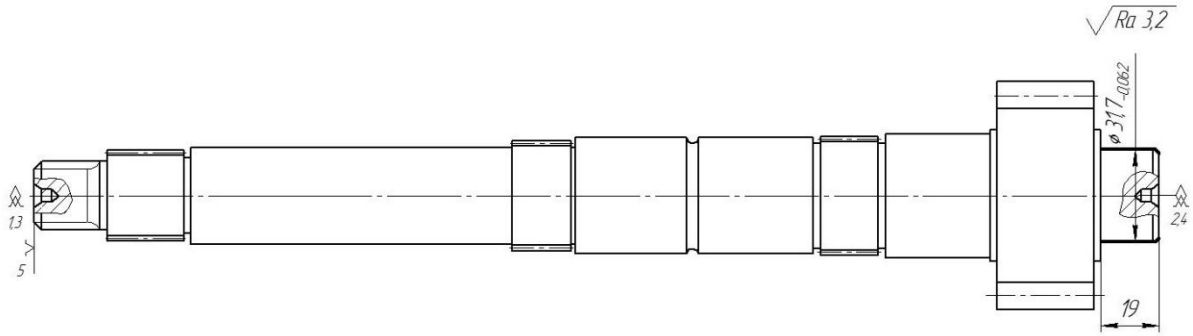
Схема закріплення вала під час шліфування опорної шийки.
